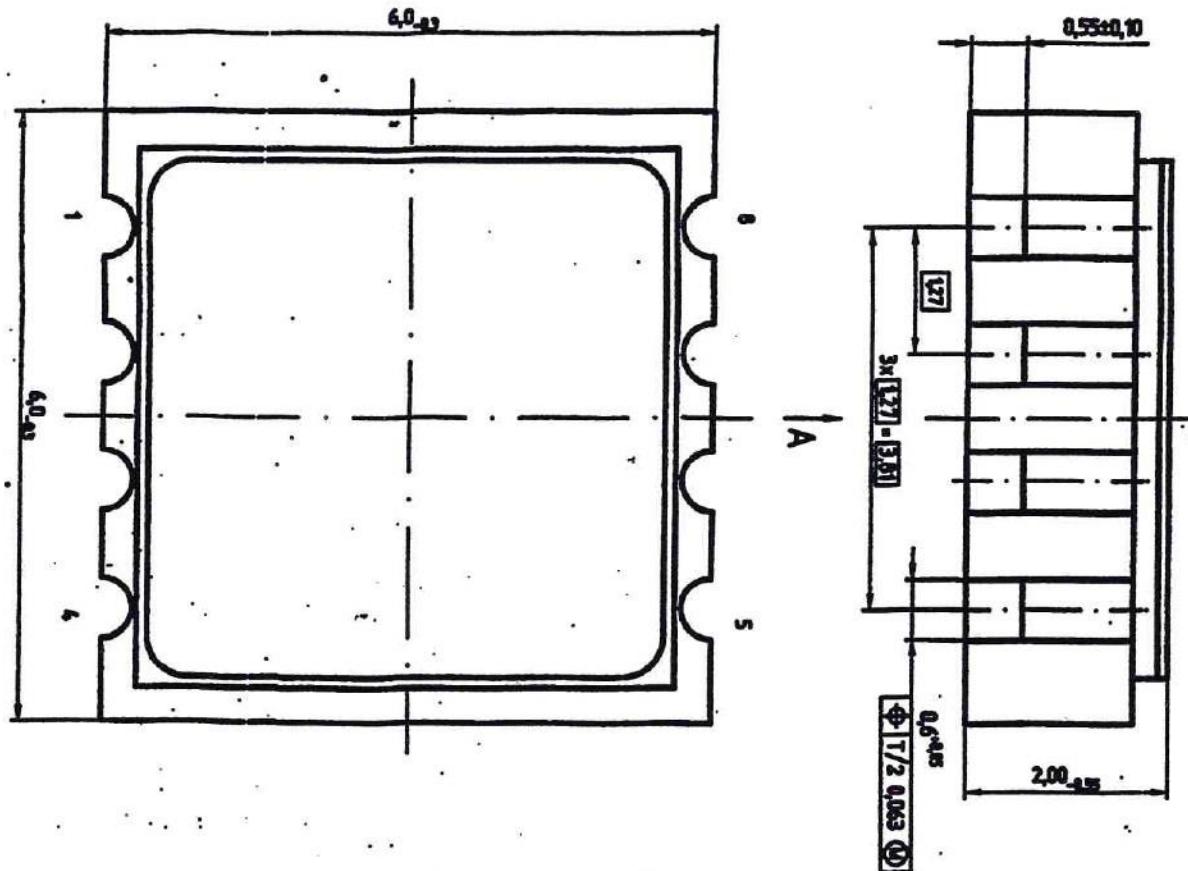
Габаритный чертеж корпуса 5205.8-2
